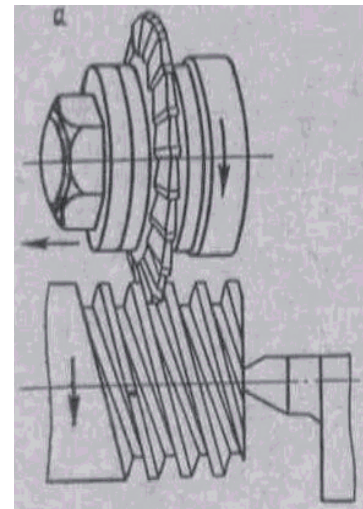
Нарезание винтовой поверхности дисковой фрезой
